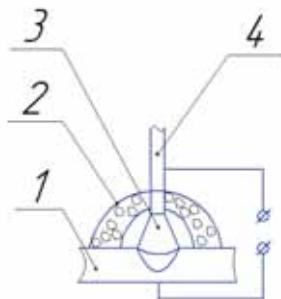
Сварка под слоем флюса: 1 – деталь; 2 – слой флюса; 3 – дуга; 4 – электрод
